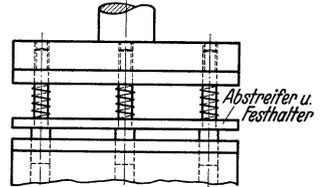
Bolzenführung der Stempel als Abstreiferführung und Aufhängung.
